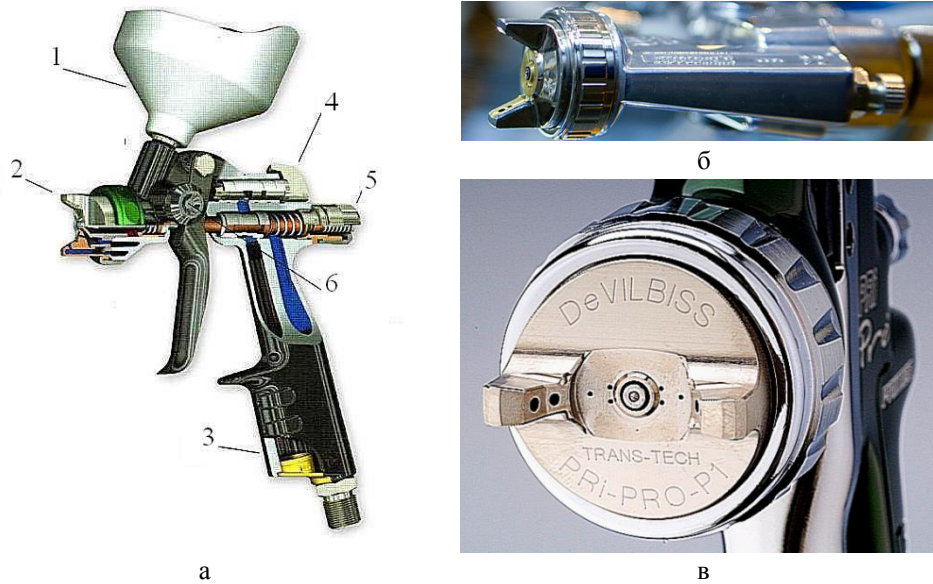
Компонування (а), загальний вигляд розпилювальної головки (б) та сопла (в) пневматичного фарборозпилювача: 1 – бачок; 2 – розпилювальна головка; 3 – рукоятка; 4 – регулятор подачі стисненого повітря; 5 – регулятор подачі ЛФМ; 6 – регулятор форми факела розпилення ЛФМ
